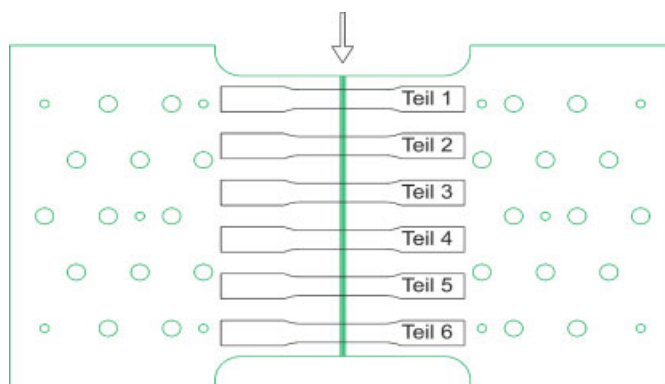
Lage der Teilproben auf dem verschweißten Blech
